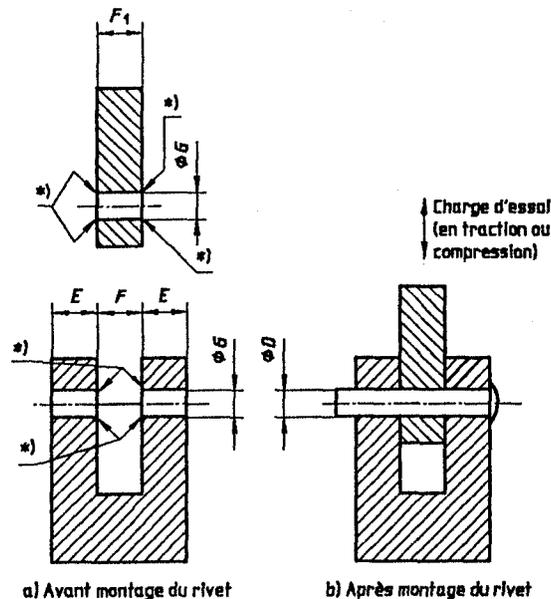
Dispositif d'essai à monter sur la machine d'essai
